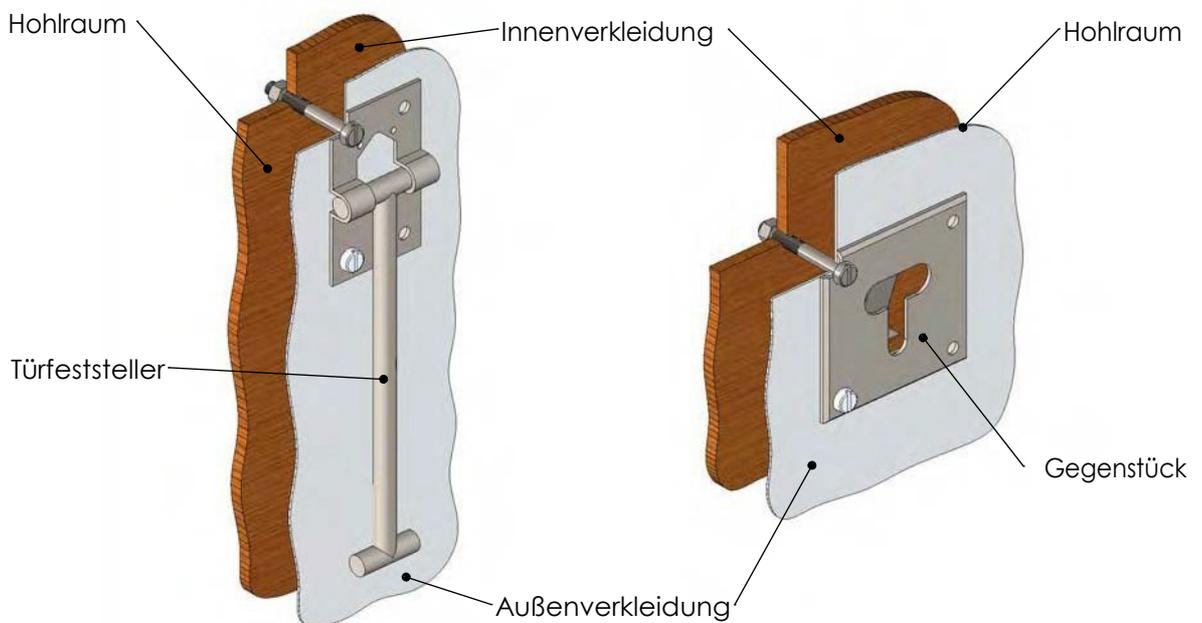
Befestigung mit im Laderaum gesicherten Schrauben
